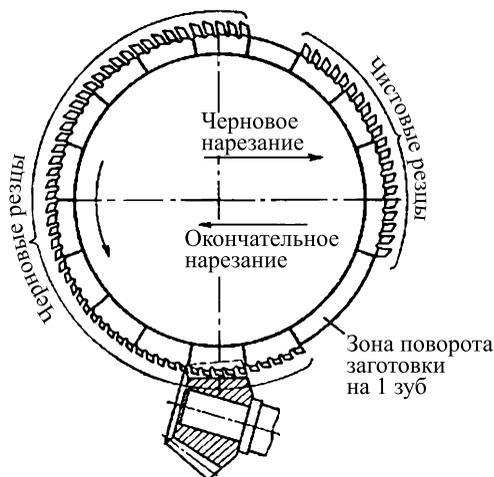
Схема кругового протягивания зубьев конического колеса
